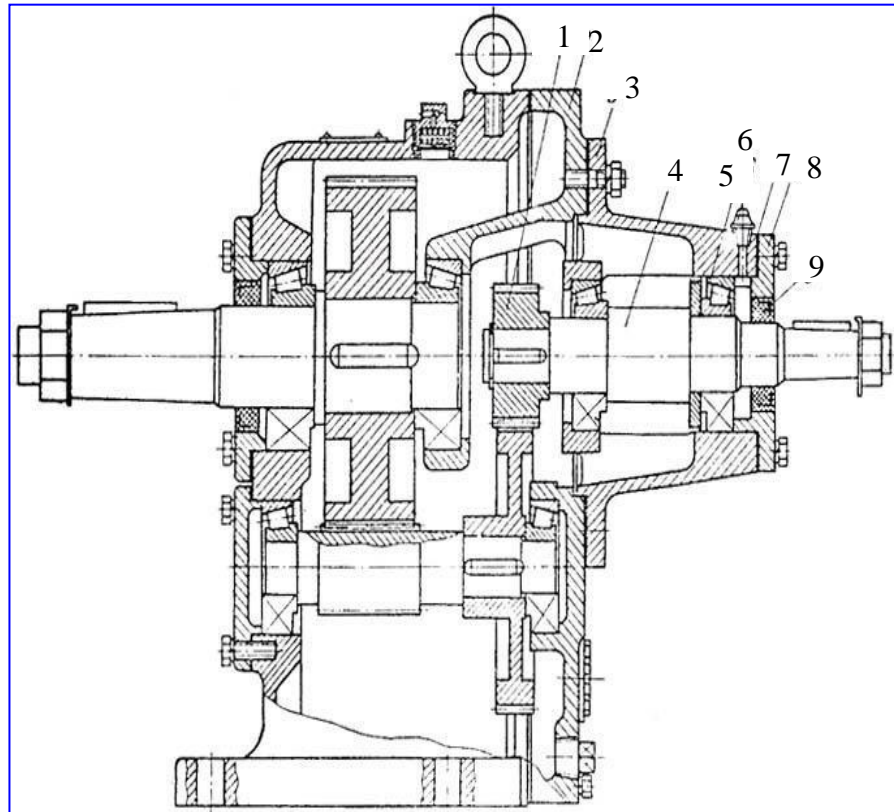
Загальний вигляд вертикального співвісного редуктора:
